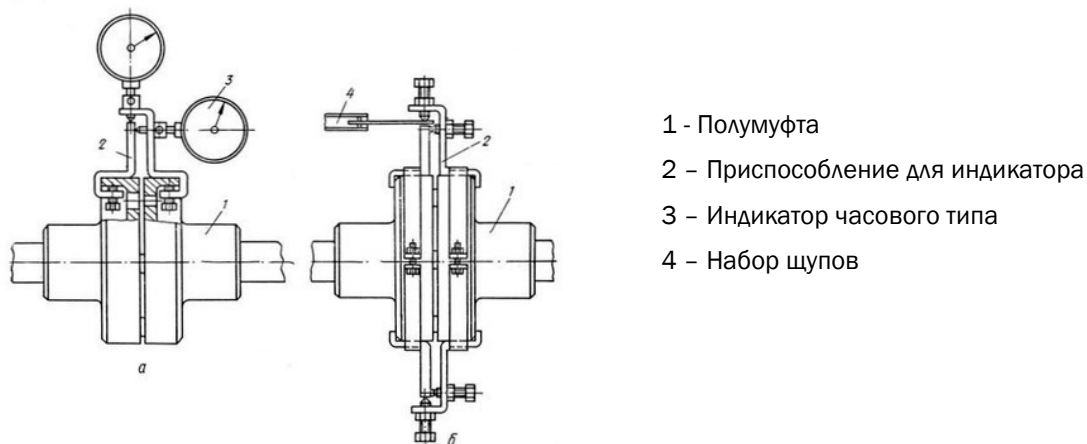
Приспособления для контроля центровки по полумуфтам:
